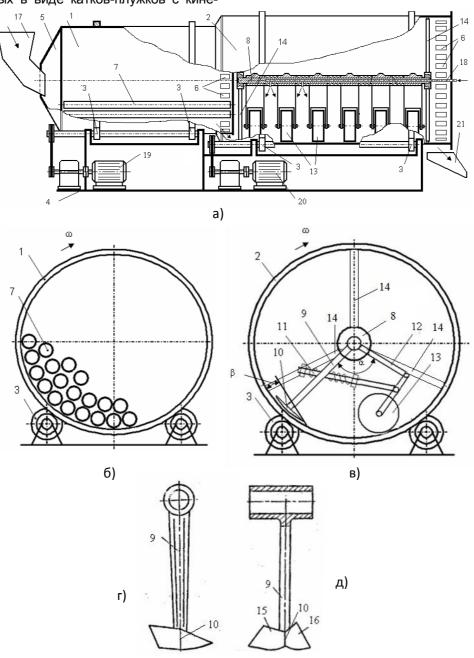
Каскадный барабанный смеситель непрерывного действия: а) общий вид (фронтальный разрез), б) поперечный разрез первой секции, в) поперечный разрез второй секции, г) фронтальный вид плужка, д) профильный вид плужка.
